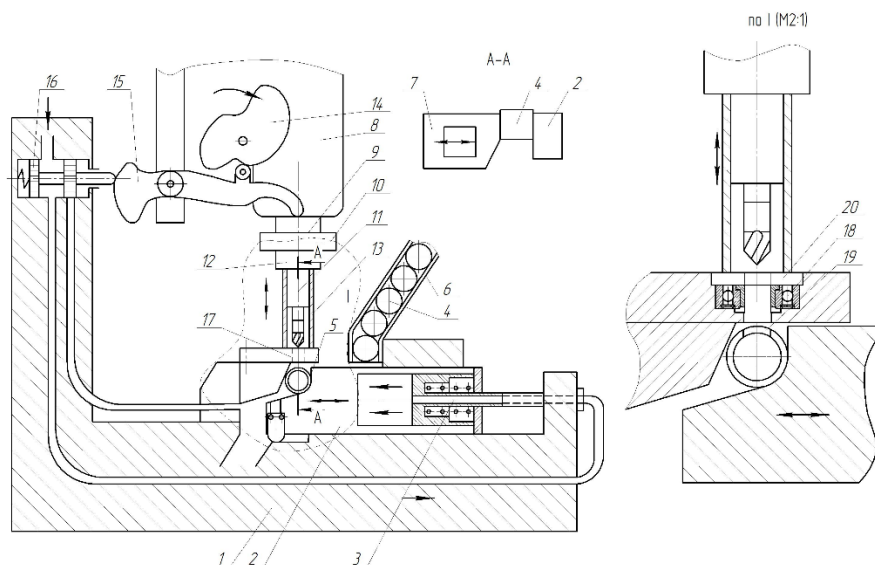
Пневматичний автоматизований пристрій для свердління і нарізання різі в трубчастих заготовках
